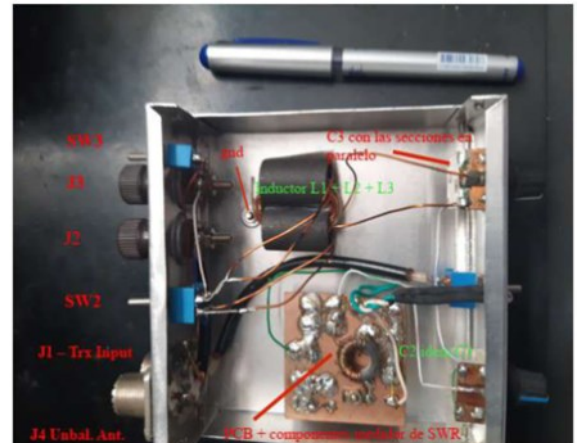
Disposición de los componentes principales (PCB SWR, C2, C3, Induc. L1+L2+L3)
